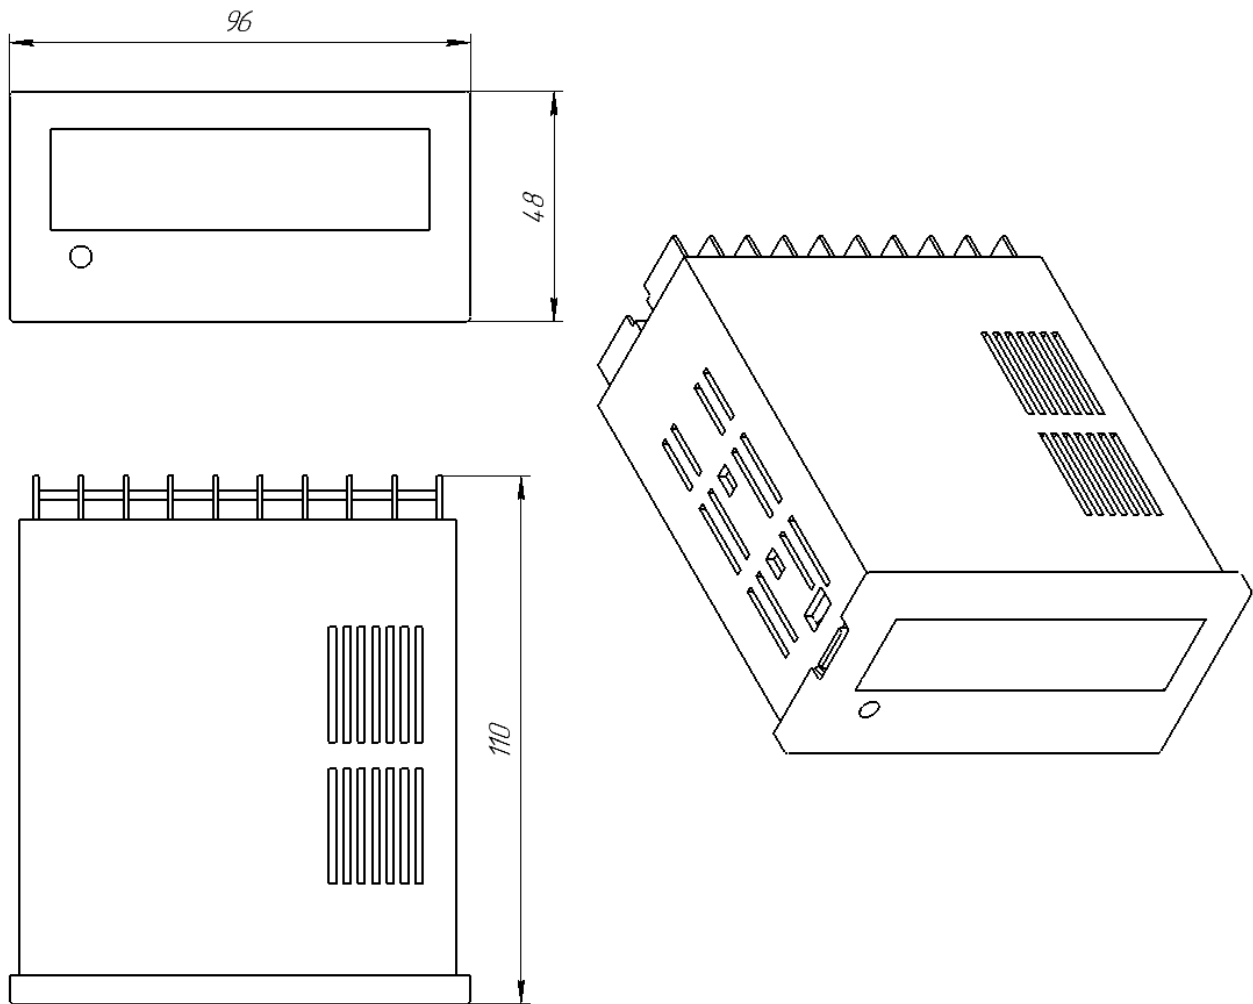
Габаритные размеры счётчика моточасов WTM-20
